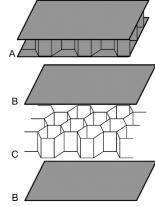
Leichtbaukomponente in Sandwichbauweise mit Wabenkern
